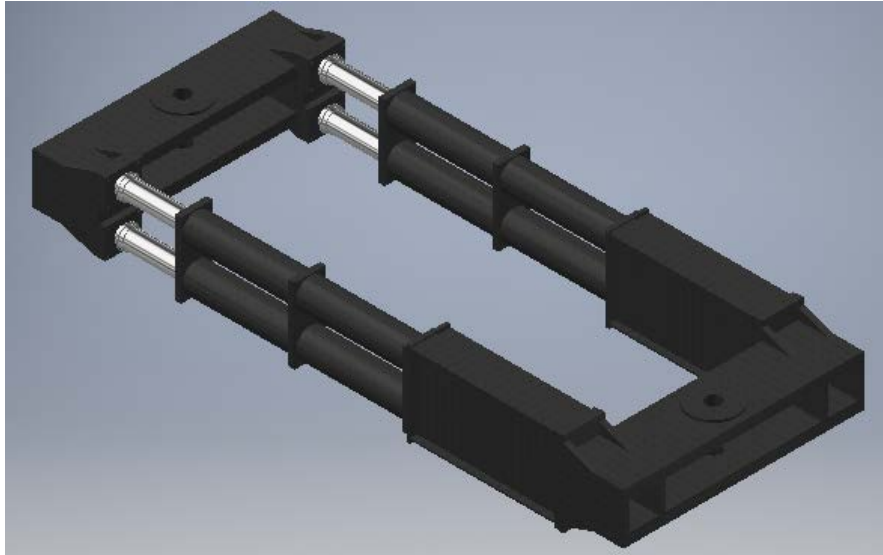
Vista isométrica máquina cabeçotes, pistões e vigas de 3 metros
